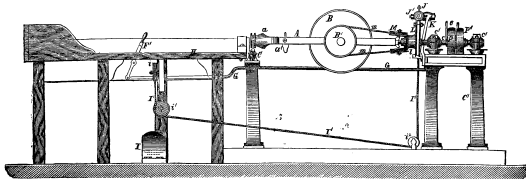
Tabaks-Spinnmaschine. Seitenansicht.
